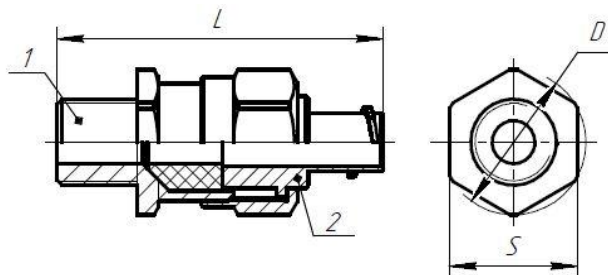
Общий вид кабельного ввода ВН с фитингом для крепления металлорукава.
